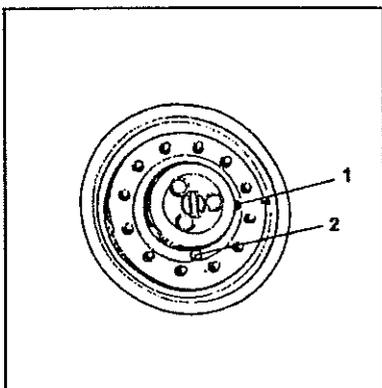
Engranaje planetario - posición de llenado de aceite
